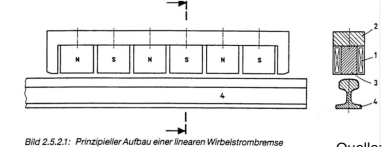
Prinzipieller Aufbau einer linearen Wirbelstrombremse
